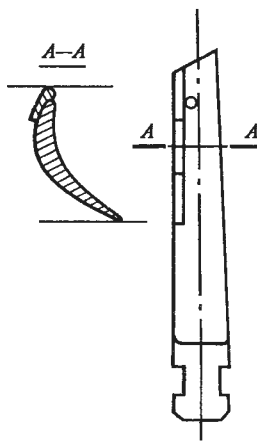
Рабочая лопатка со стеллитовыми накладками
